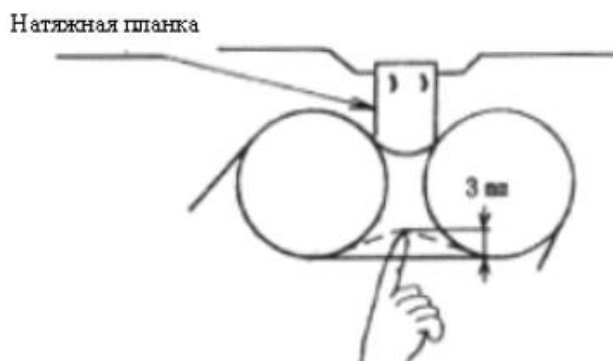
Регулировка цепи с помощью натяжной планки
